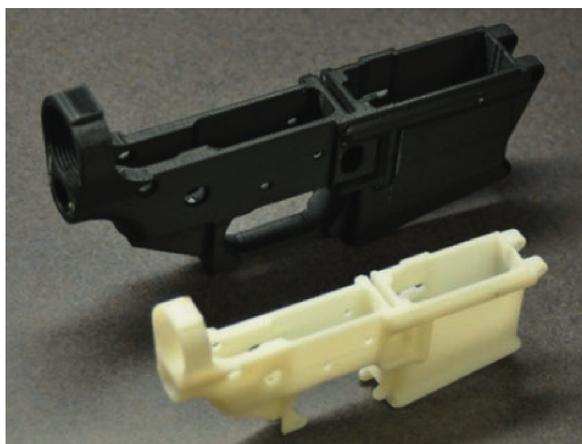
Распечатанный нижний ресивер винтовки AR-15
